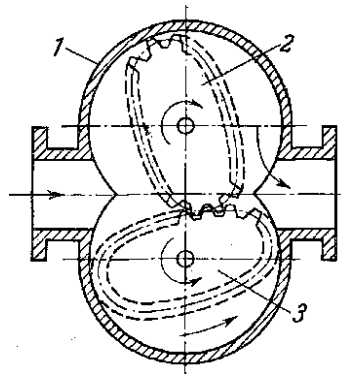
Схема лічильника рідини з овальними шестернями
